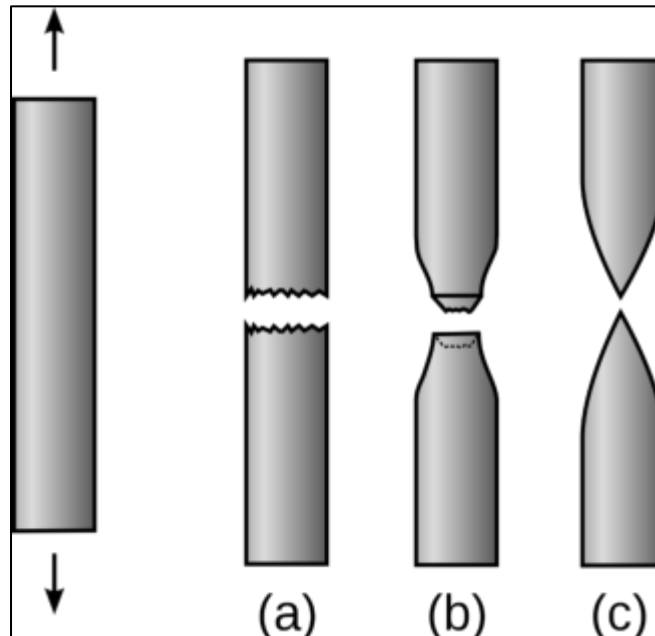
Aspecto esquemático de barras redondas de metal después de la prueba de tracción. (a) Fractura frágil (b) Fractura dúctil, c) fractura completamente dúctil
